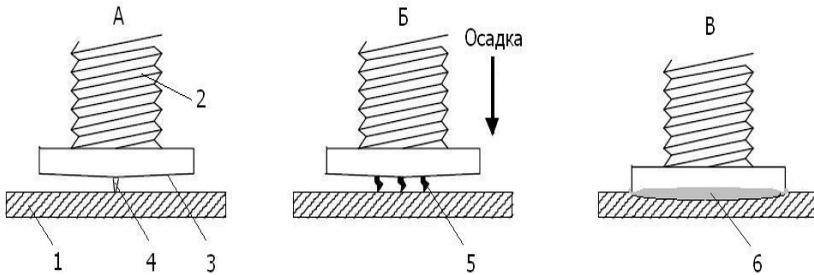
Схема приварки стержня с использованием энергии, запасенной в конденсаторе (CD Stud Welding)
